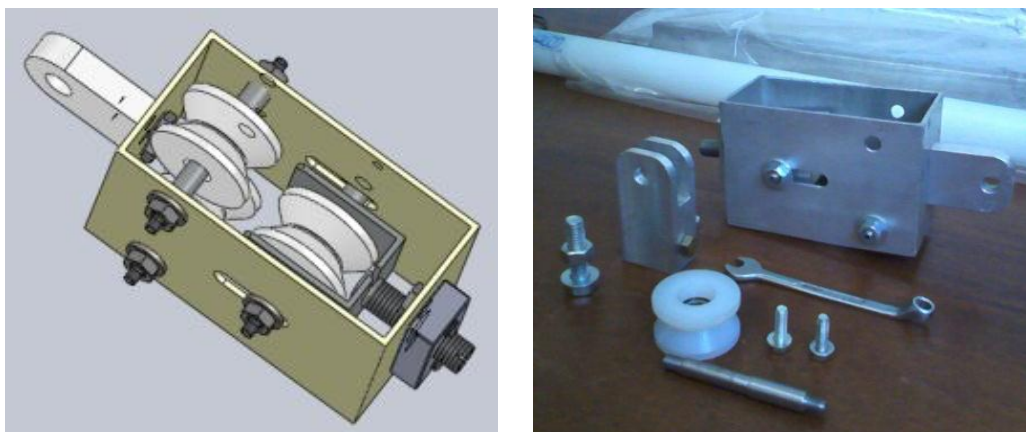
Componente móvel inicial do dispositivo de soldagem
